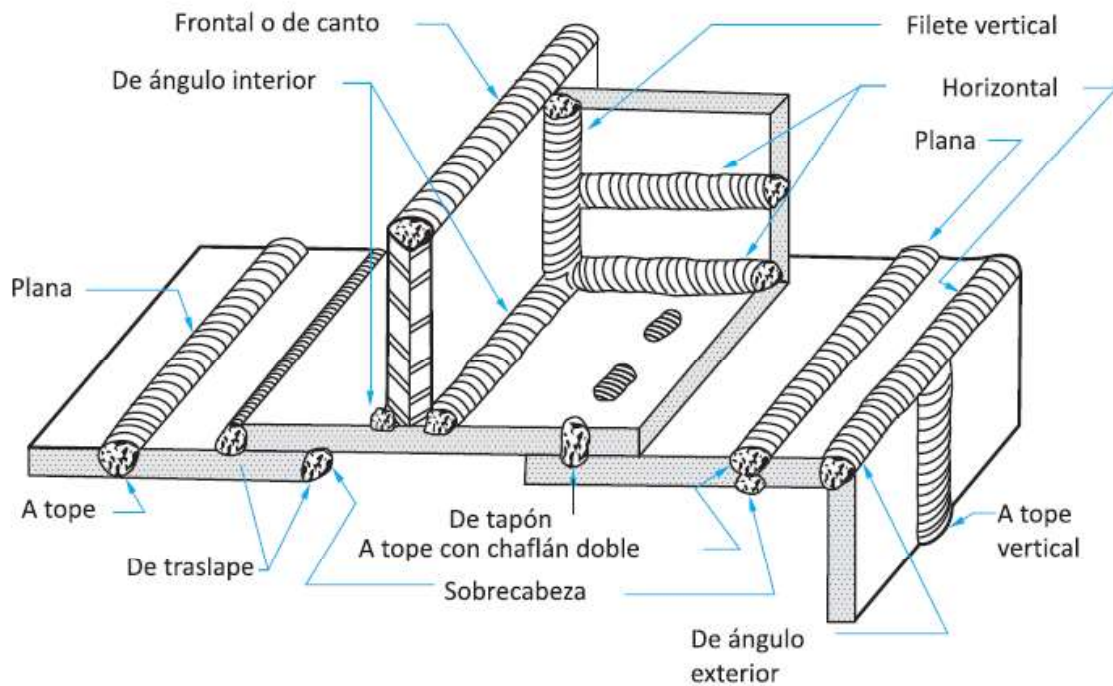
Diversas juntas y posiciones de soldadura.
